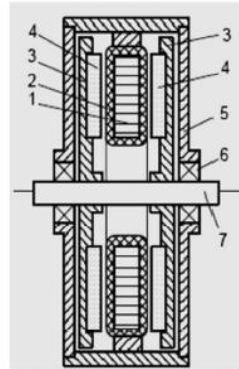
Descriptif de la machine à flux axial stator externe [13].
